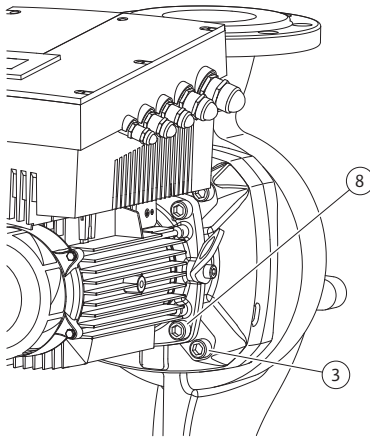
Fixarea opțională a ansamblului motor cu rotor hidraulic
